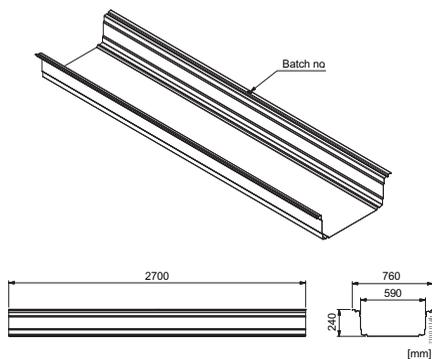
Поперечина подвесной платформы, размеры и нагрузки
